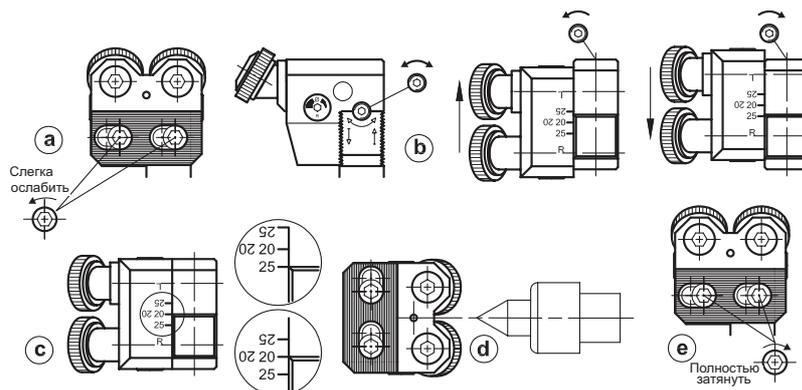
Продолжение Руководство по эксплуатации фрезеральных накаток 290242
